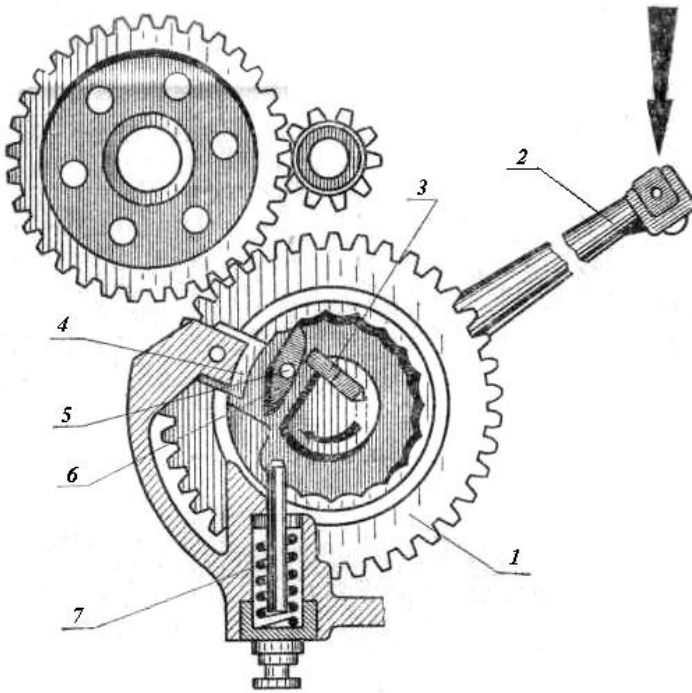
Пусковий механізм із собачкою і храповою шестернею внутрішнього зачеплення:
